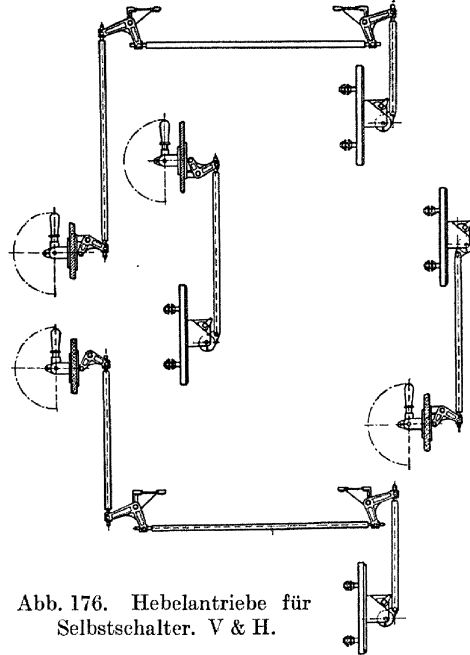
Hebelantriebe für Selbstschalter. V & H.
